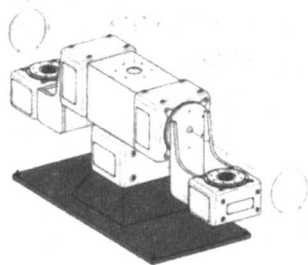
五轴二工位 L 型焊接变位机
